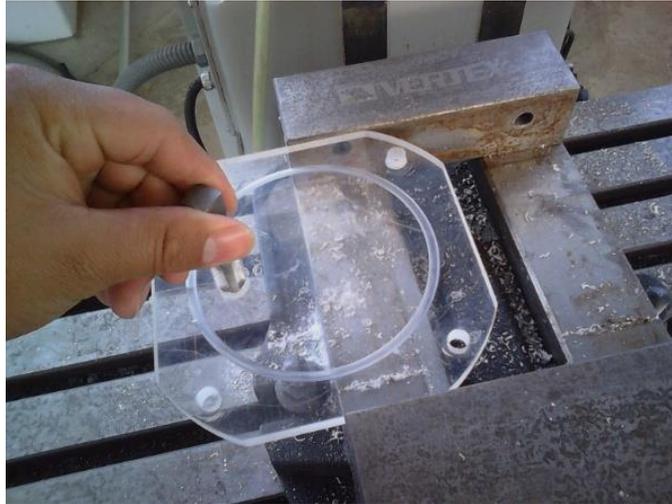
Manufactura del componente tapa de acrílico en fresadora cnc.
